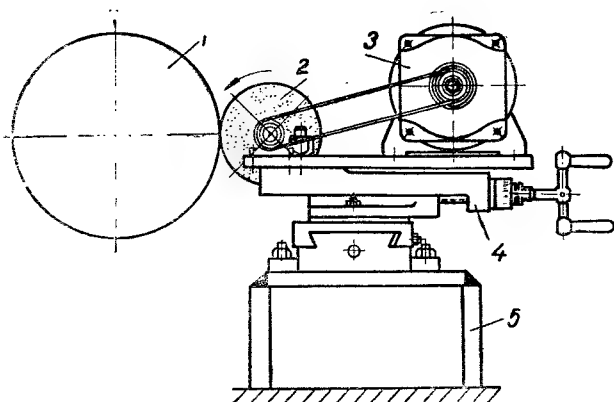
Приспособление для шлифовки контактных колец ротора (при вращении ротора в собственных подшипниках):
